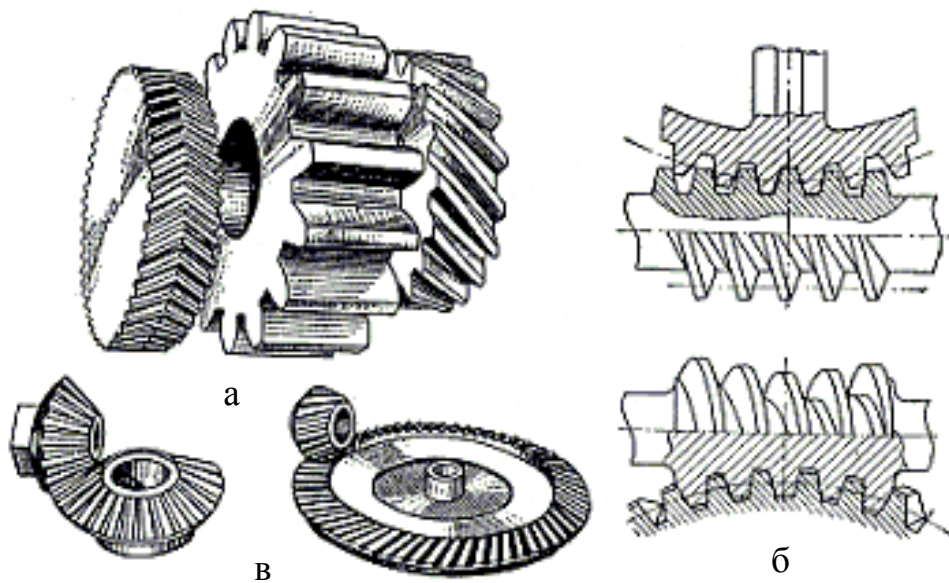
Види зубчастих коліс: а – циліндричні з прямими, похилими і шевронними зубами; б – черв'ячні з циліндричними і глобоїдними черв'яками; в – конічні з прямими і спіральними зубами.
